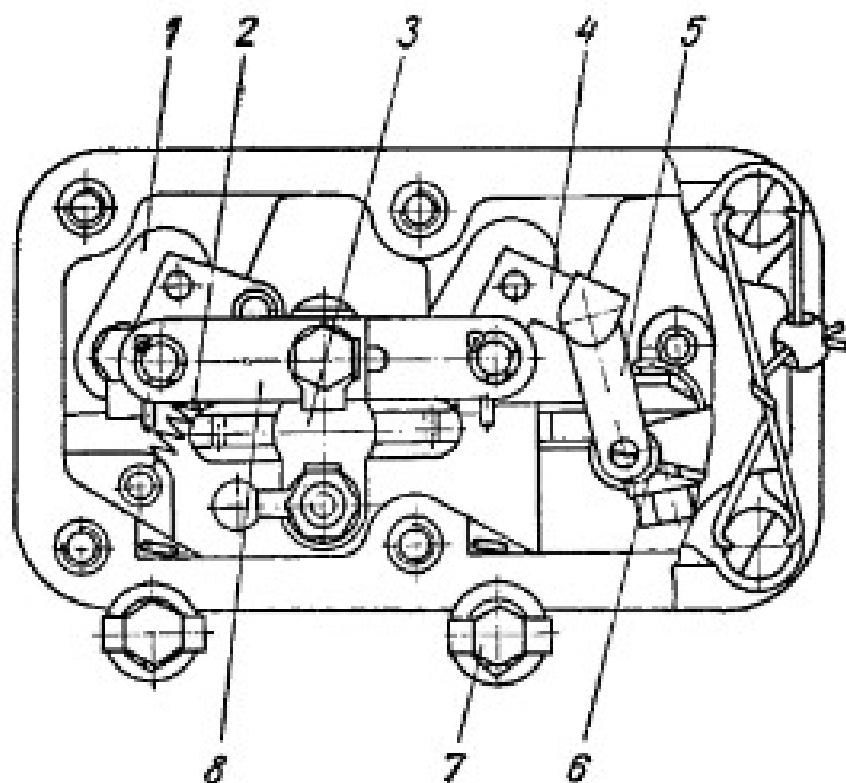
Система управления дозаторами (вид сбоку на топливный насос при снятой крышке):
